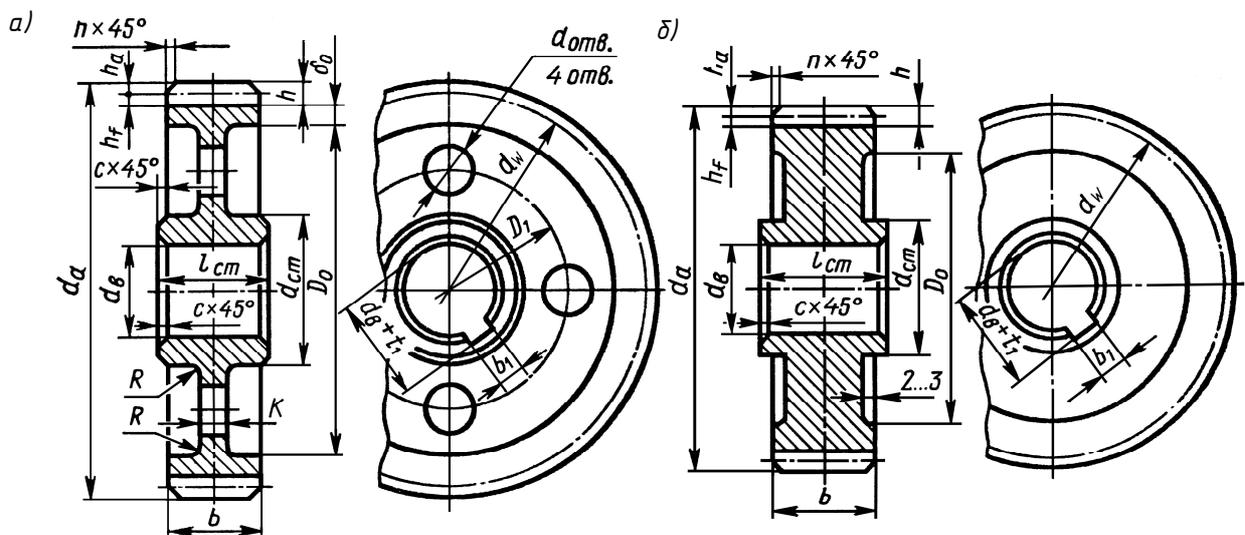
Цилиндрическое зубчатое колесо:
